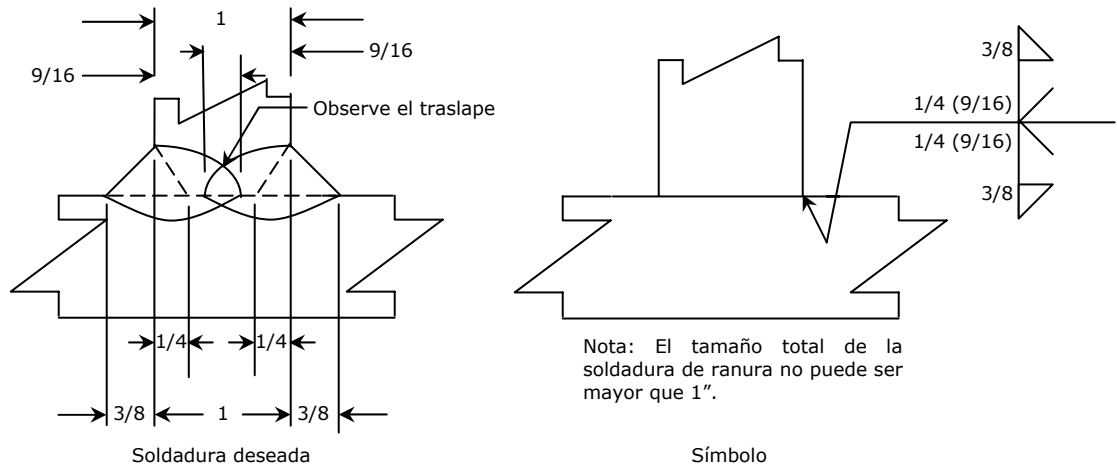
Símbolo de soldadura combinada para ambos lados de la unión
